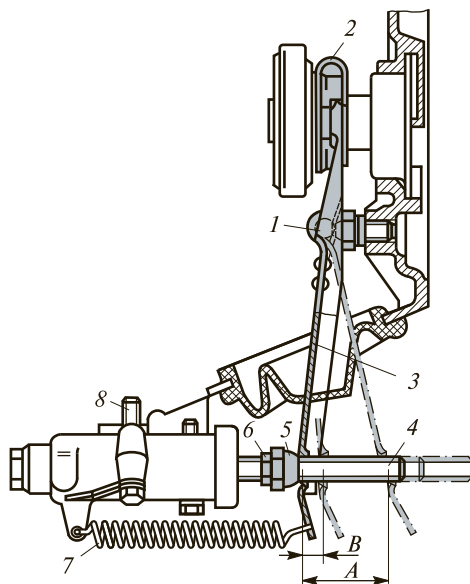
Регулировка свободного хода штока рабочего цилиндра сцепления:
